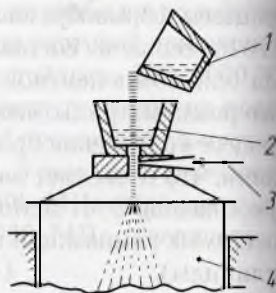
Схема установки для распыления порошков: 1 — тигель с расплавом; 2 — керамическая воронка; 3 — форсунка; 4 — приемный бункер
